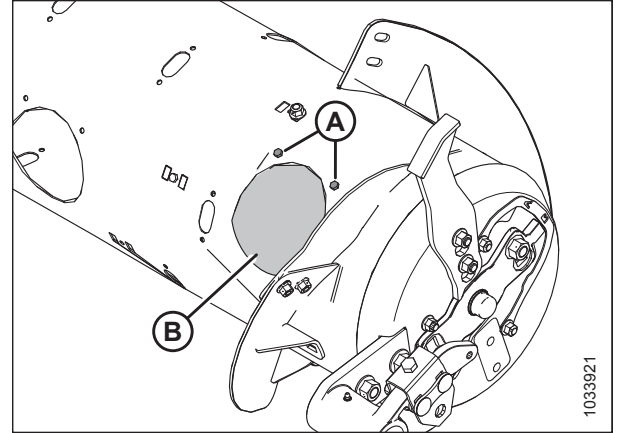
Cubierta de acceso al sinfín: lado derecho
